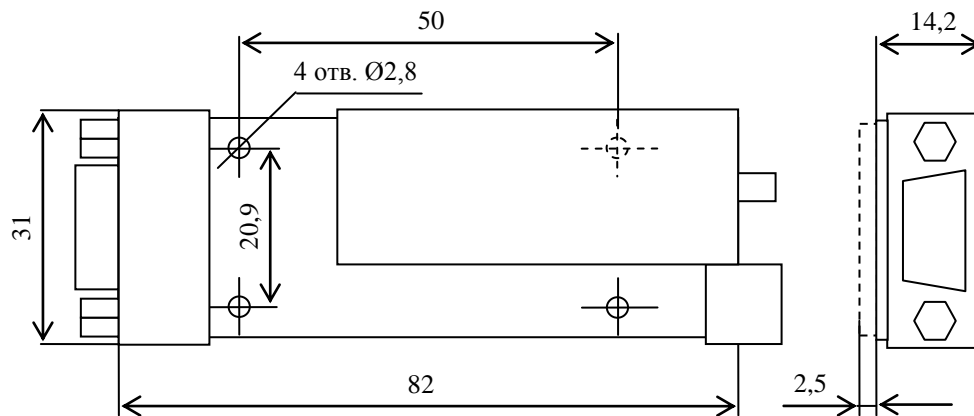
Габаритный чертёж бескорпусного варианта радиомодема РМД400L-UP0
